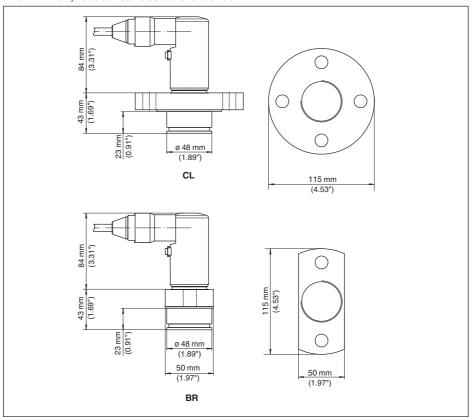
VEGABAR 82, Flanschanschluss für die Papierindustrie: CL = absolut frontbündig für Stoffauflauf, BR = absolut frontbündig für Stoffauflauf (Flansch 2-fach abgeflacht)
